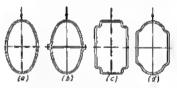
Secciones de vigas de paredes delgudas de elevada ri-
